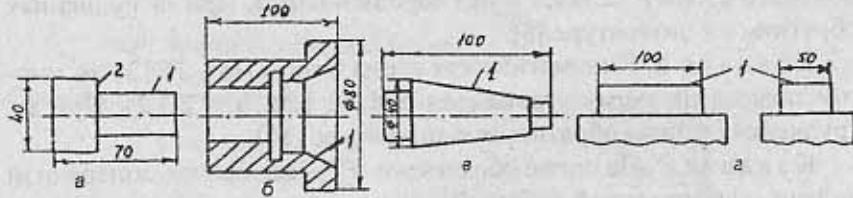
Детали, обрабатываемые на шлифовальных станках с ЧПУ
